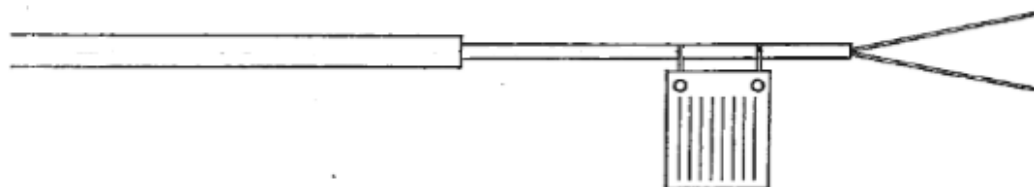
Чертеж термопреобразователя сопротивления платинового 902821/81-386-2001-1-5-30-000-00-11-1300/362
